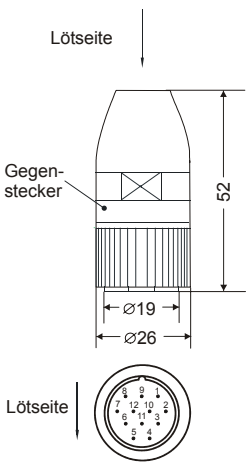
Sicht auf HIPERFACE-Gegenstecker der Serie RC (Gewinde M23)
